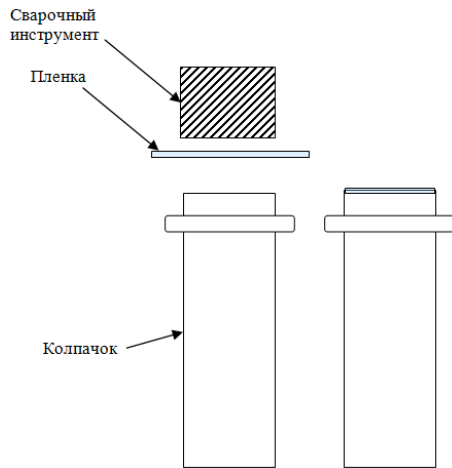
Схема сварки для плоского сварочного инструмента (СИ1)
